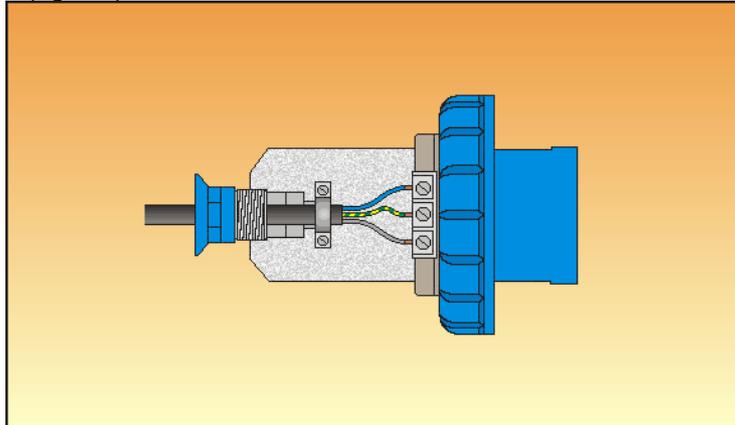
Collegamento delle spine – Il conduttore giallo-verde di terra deve essere più abbondante rispetto a quelli di fase e di neutro
